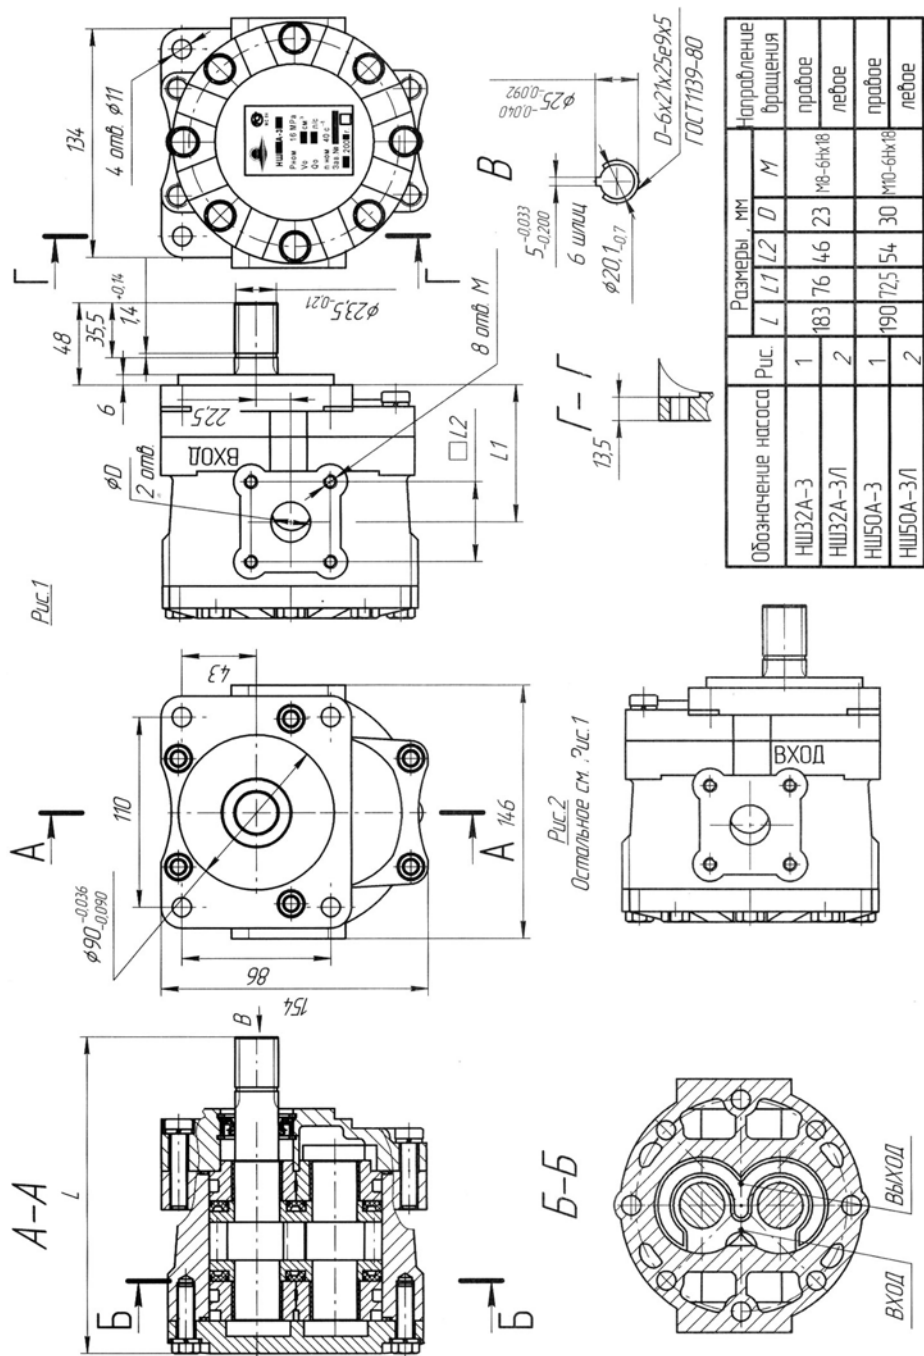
Габаритный чертеж насосов НШ32А-3(Л) и НШ50А-3(Л)
